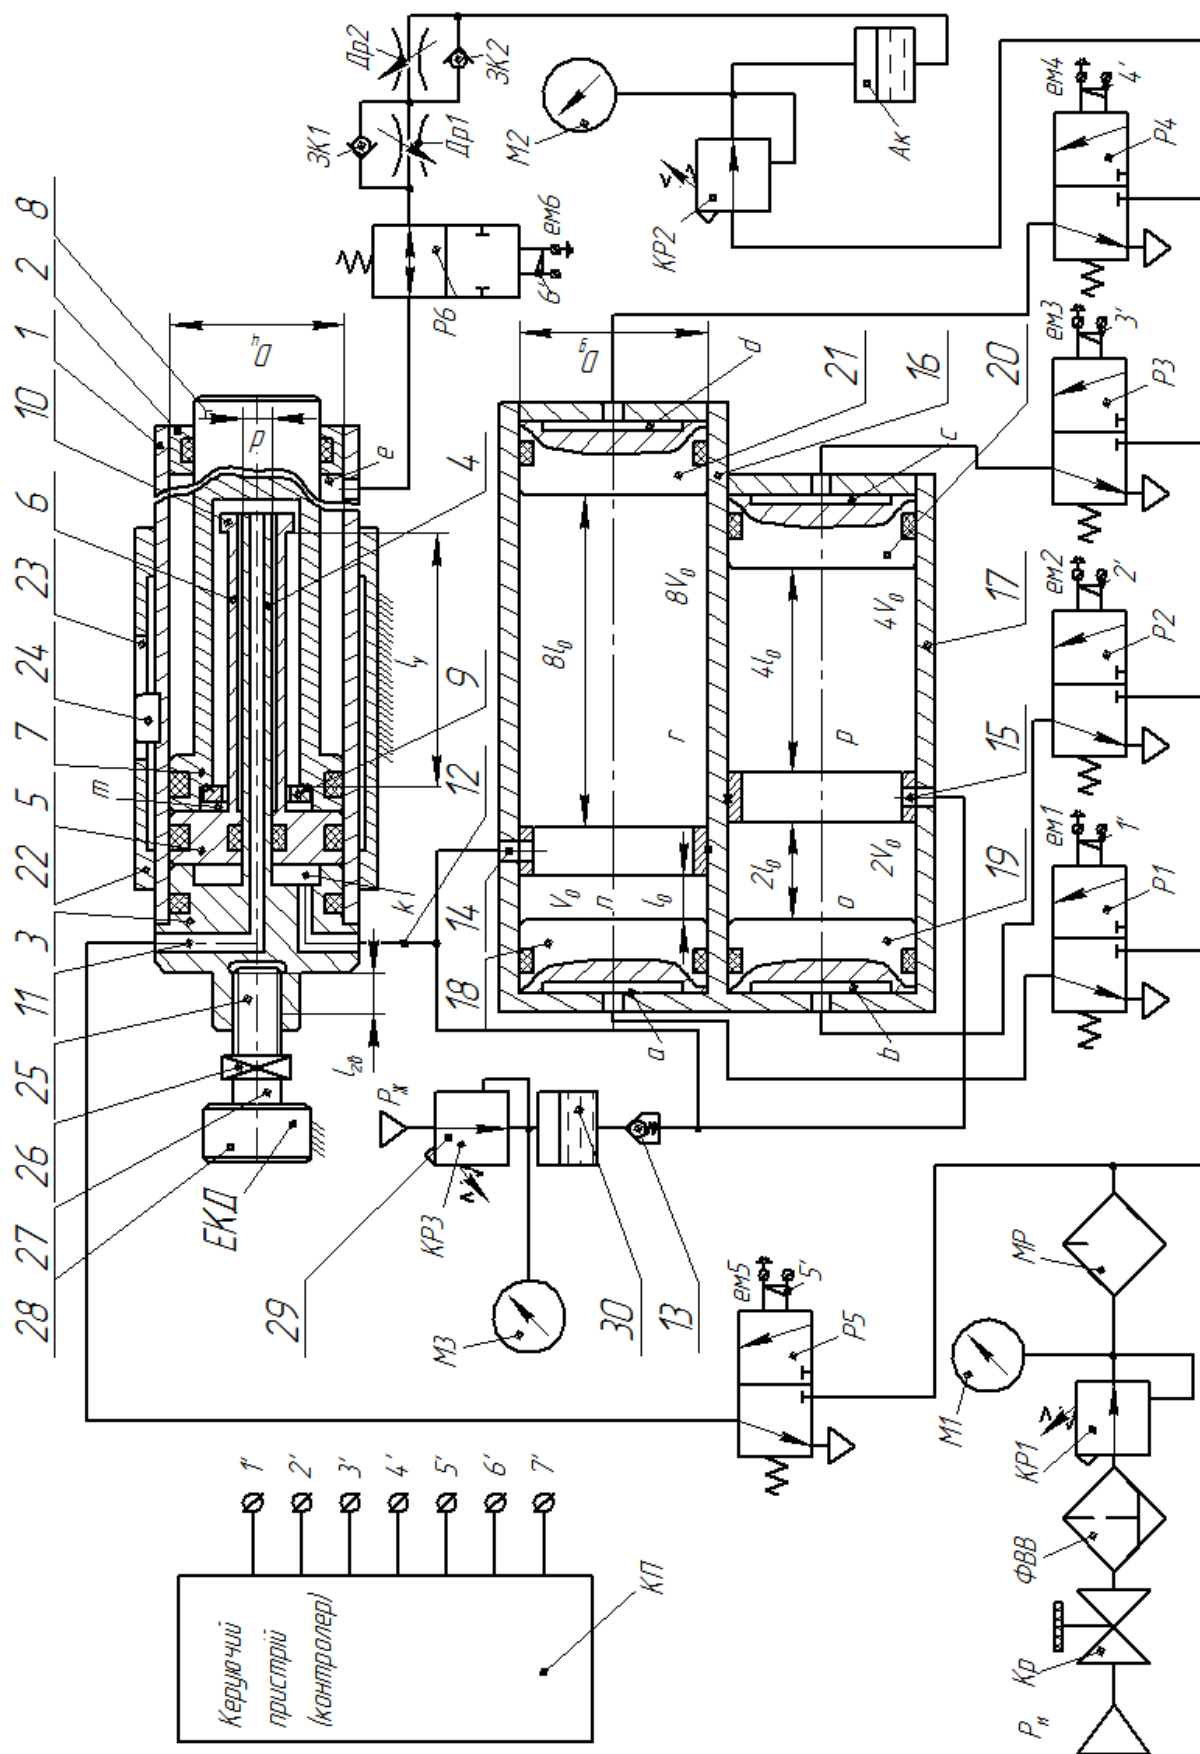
Принципова схема багатопозиційного пневмоелектричного приводу
